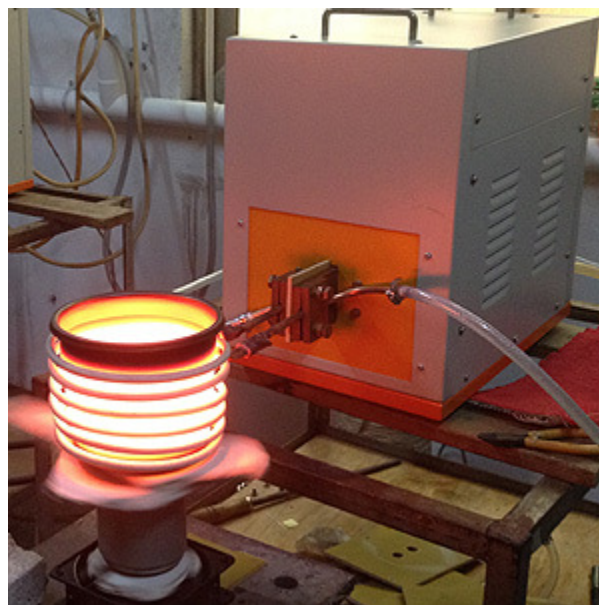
Calentador de piezas industrial que utiliza el principio de inducción
